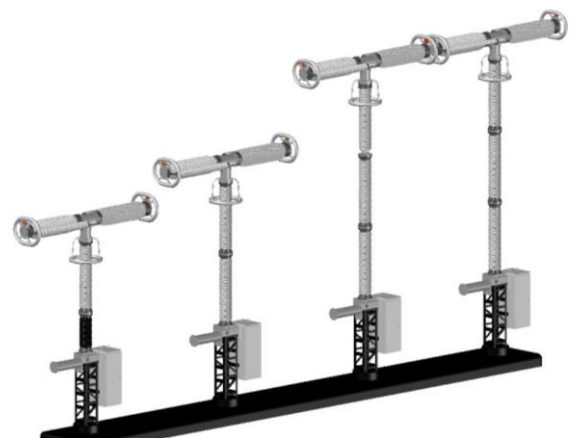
CAD-модель ВГТ выключателя 110, 220, 500 и 750 кВ
